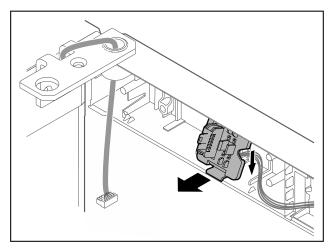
La position de montage du support de connecteur peut être tournée de 180°.
